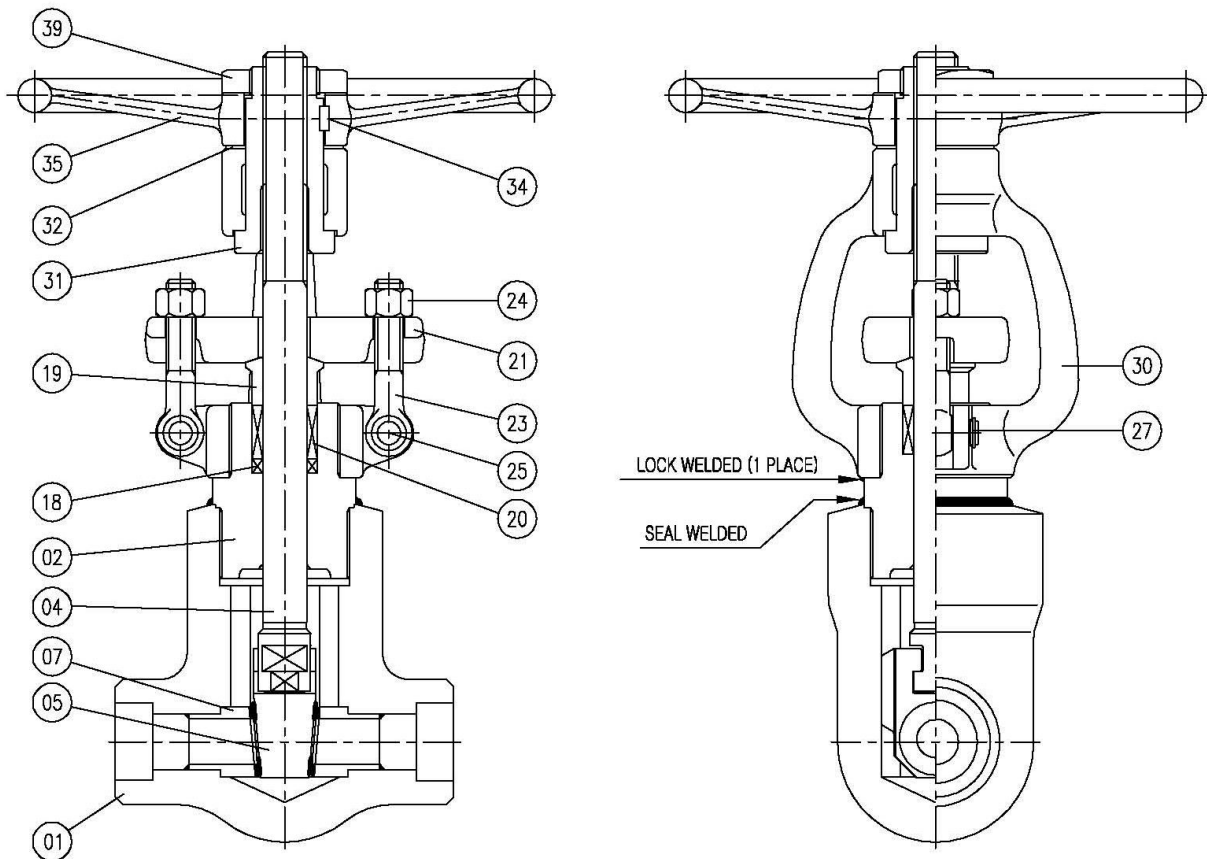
SCREWED BONNET & SOLID WEDGE DISC GATE VALVE
